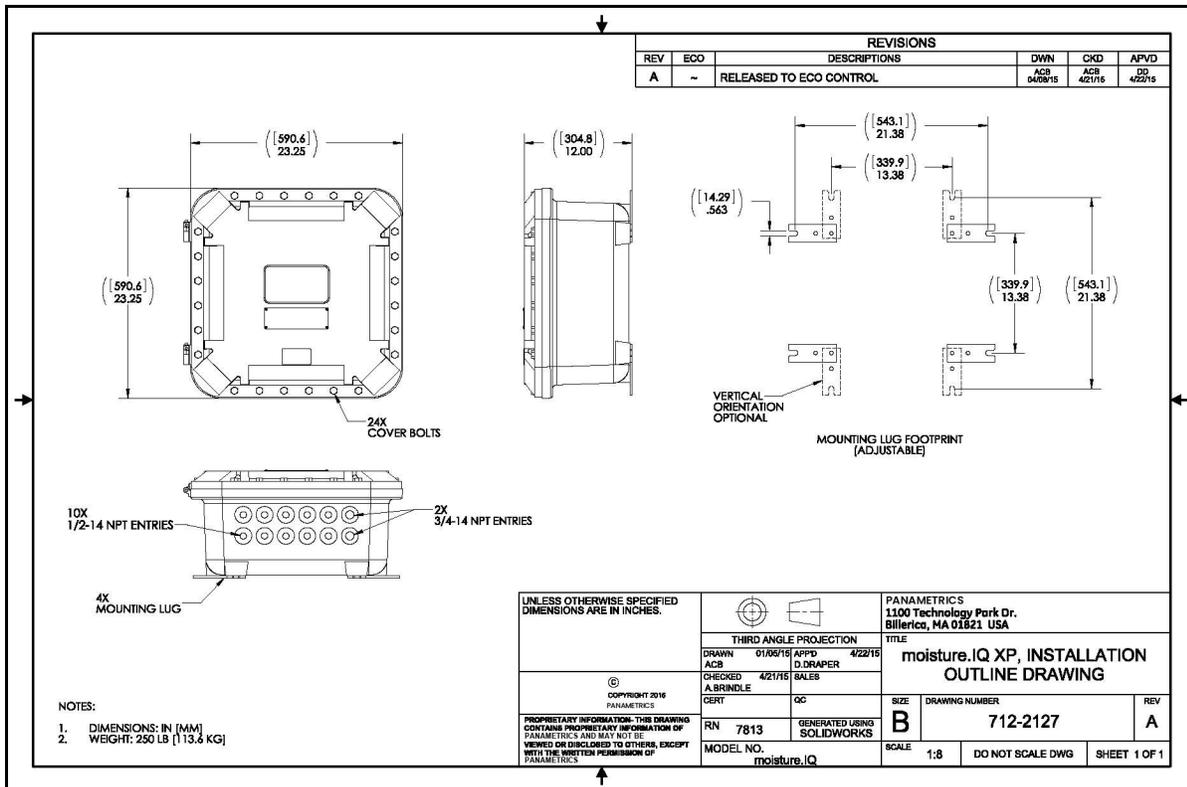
Plano esquemático de instalación XP (Plano 712-2127_revA, SH 1 de 1)
